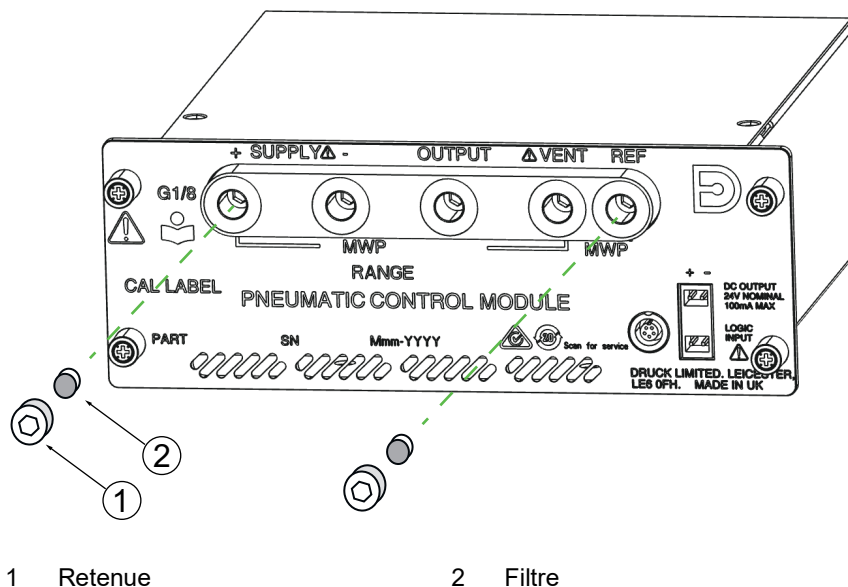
Remplacement du filtre du module de commande pneumatique
